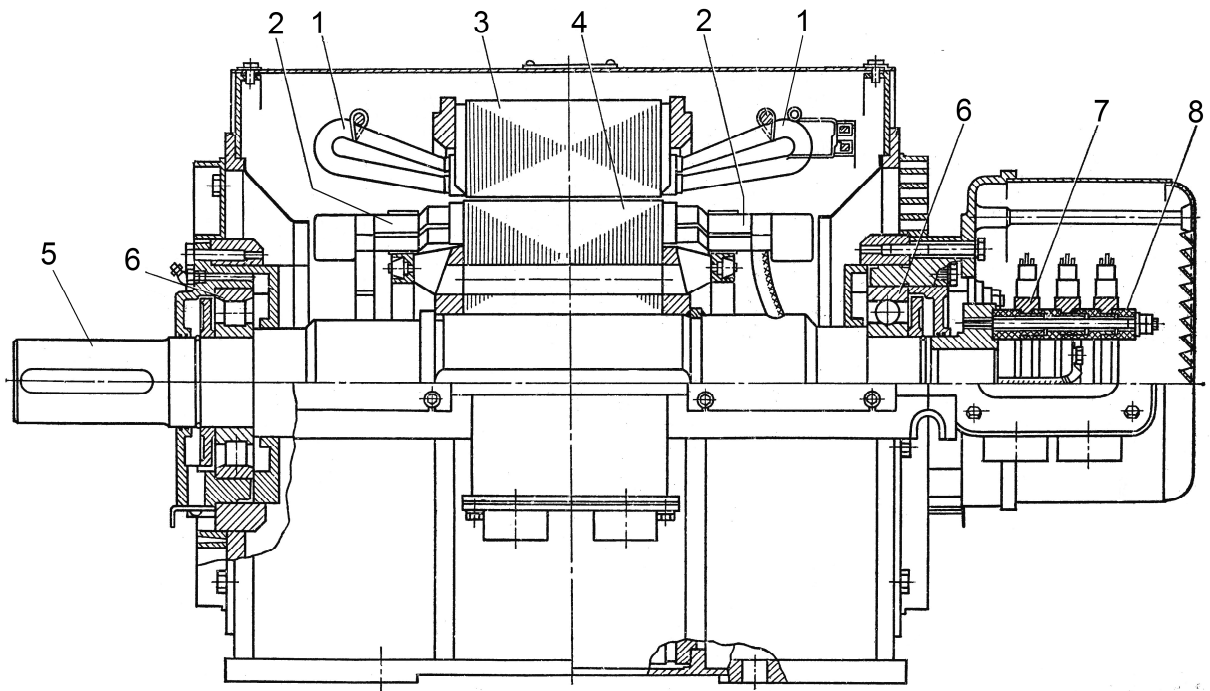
Асинхронный двигатель серии 4А с фазным ротором и степенью защиты IP23: 1, 2 – обмотки статора и ротора; 3, 4 – сердечники статора и ротора; 5 – вал; 6 – подшипники; 7 – контактное кольцо; 8 – изоляция контактных колец
